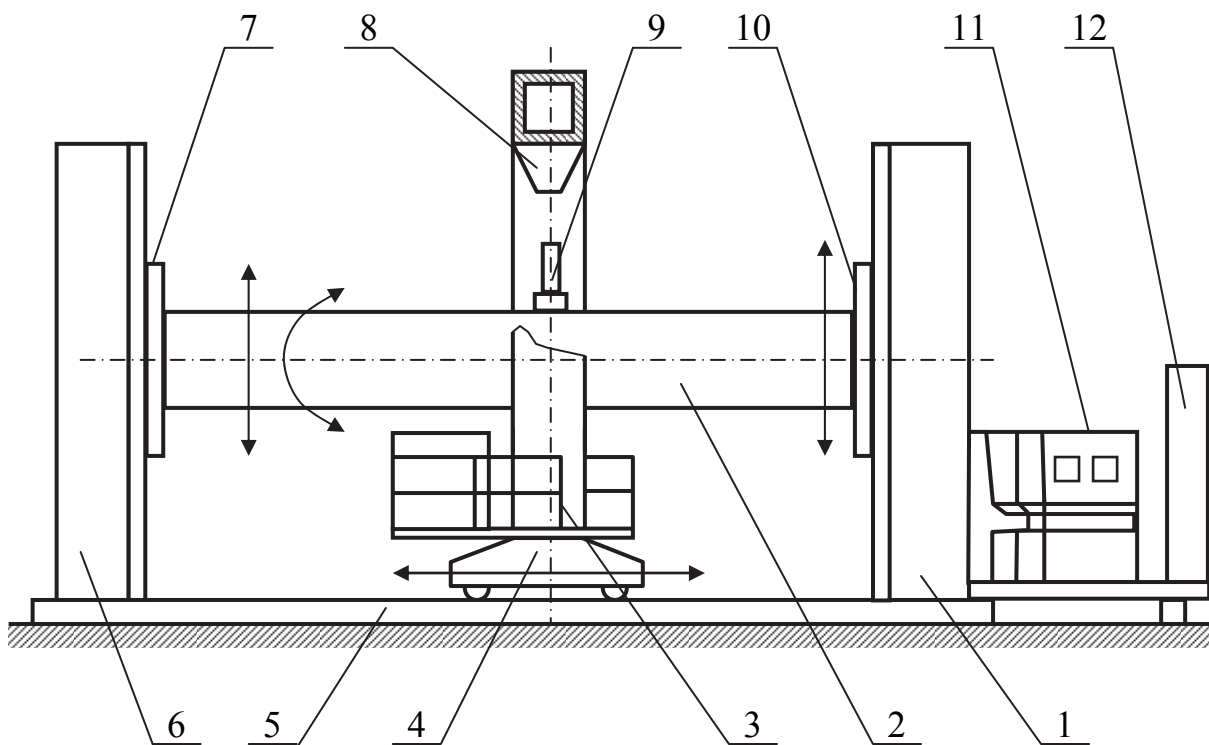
Схема конструкции клепального автомата: 1 – правая стойка; 2 – рама; 3 – станина; 4 – каретка станины; 5 – рельсовая направляющая; 6 – левая стойка; 7 – каретка левой стойки; 8 – верхний инструмент; 9 – нижний инструмент; 10 – каретка правой станины; 11 – пульт управления; 12 – распределительный шкаф
